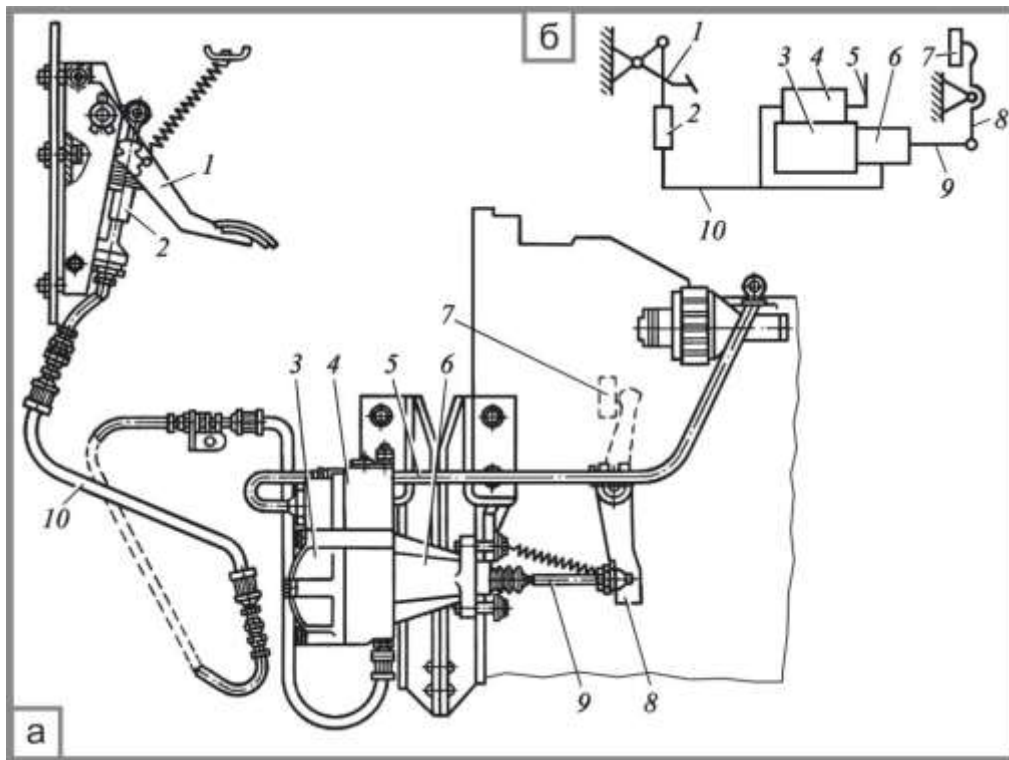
Пневмогiдравлiчний привод (а) та принципова схема приводу вимкнення (б) зчеплення: 1 – педаль; 2 – цилiндр; 3 – пневмопiдсилювач; 4 – пристрiй слiдкування; 5 – повітропровiд; 6 – робочий цилiндр; 7 – муфта вимкнення; 8 – важиль; 9 – шток; 10 – трубопровiд
